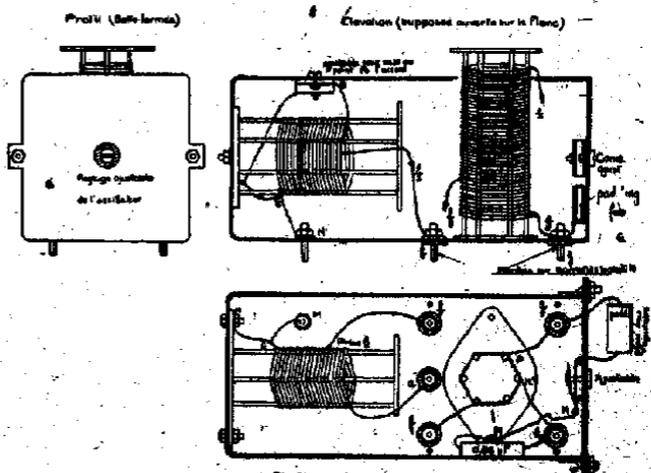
Boîte à selfs : élévation, plan et profil avec câblage des éléments.
